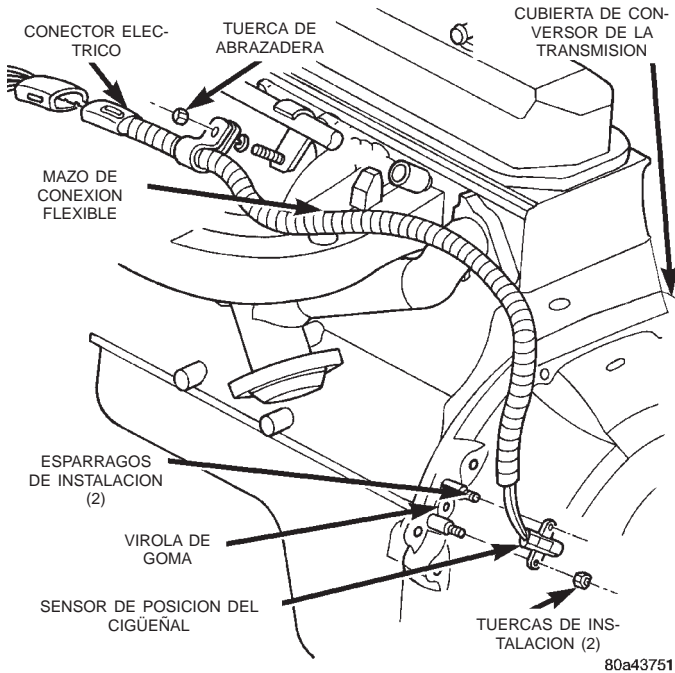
Sensor de posición del cigüeñal—Motor 2.5L
